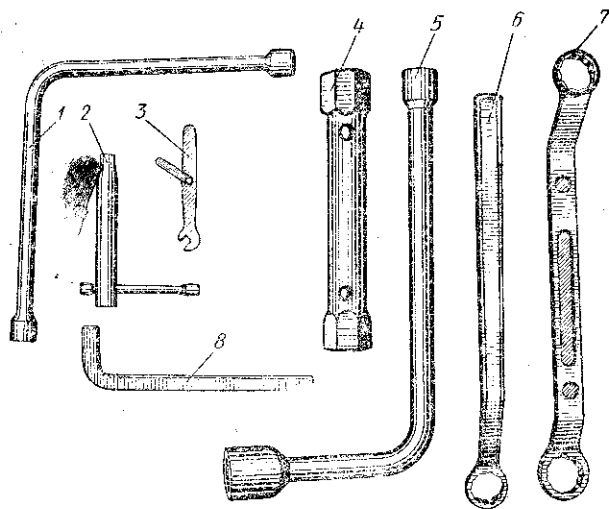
Специальные ключи комплекта инструмента, прилагаемого к автомобилю: 1 — для гаек крепления крышки клапанного механизма; 2 — для нажимного болта коромысла клапана; 3 — для распределителя зажигания (в сборе со шнупом); 4 — для свечей зажигания; 5 — для гаек крепления колес, болтов крепления щитов тормозов к картеру заднего моста и к поворотным стойкам подвески; 6 — для гаек крепления приемной трубы глушителя; 7 — для гаек стоек рессор, гайк крепления головки цилиндров и болтов крепления коробки передач к картеру сцепления; 8 — для резьбовых пробок картеров коробки передач и заднего моста
